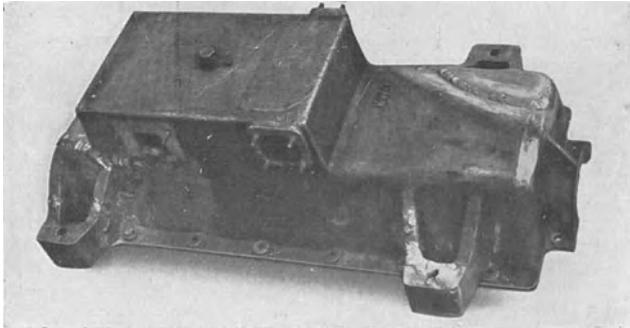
Gehäuse der Abb. 177, geschweißt, aber noch unbearbeitet.
